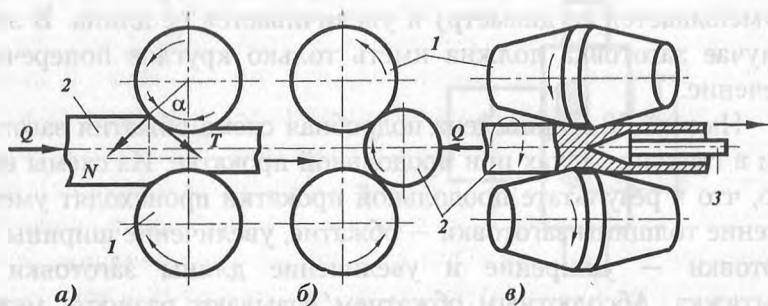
Основные виды процессов прокатки: 1 — валки; 2 — заготовка; 3 — оправка
